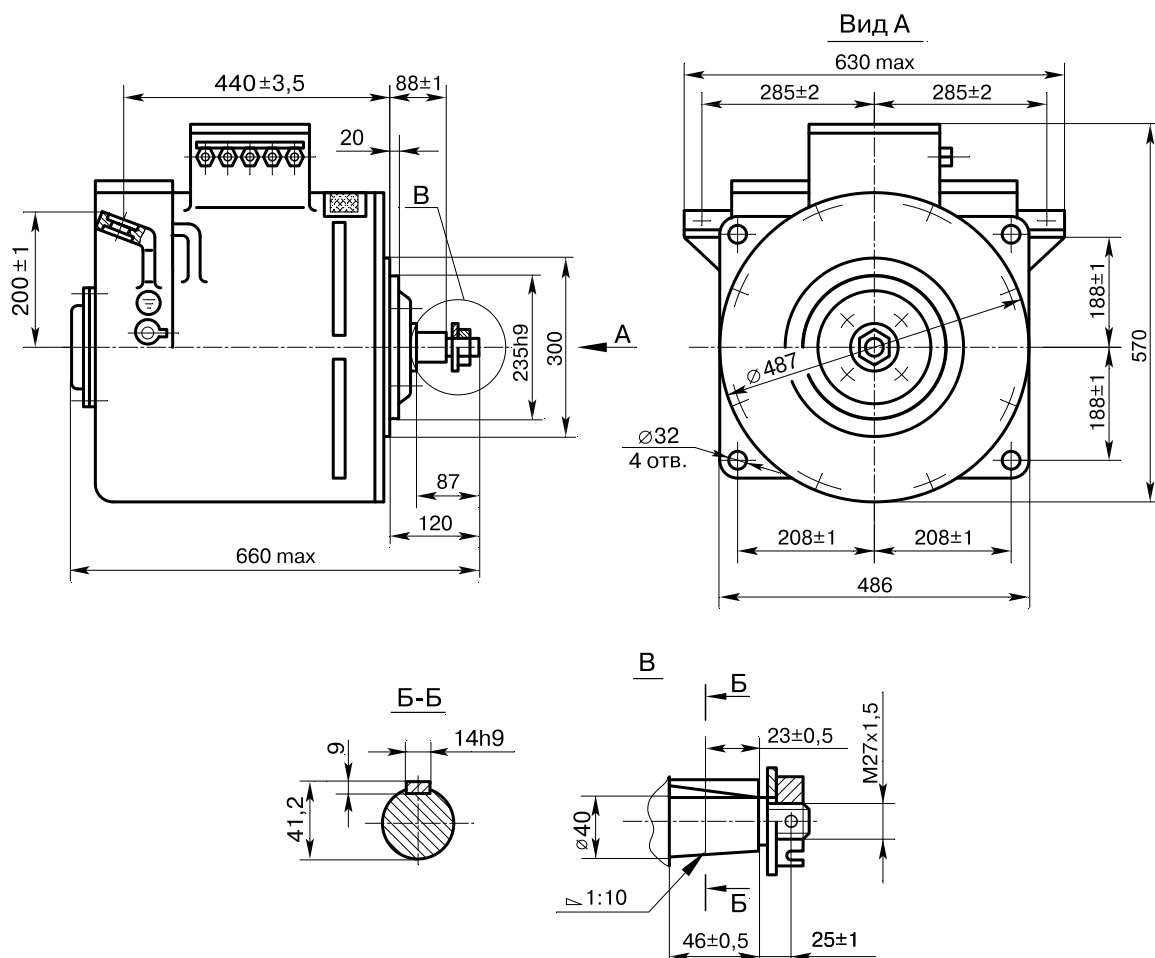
Габаритные и установочные размеры электродвигателя ДТН–12/7
